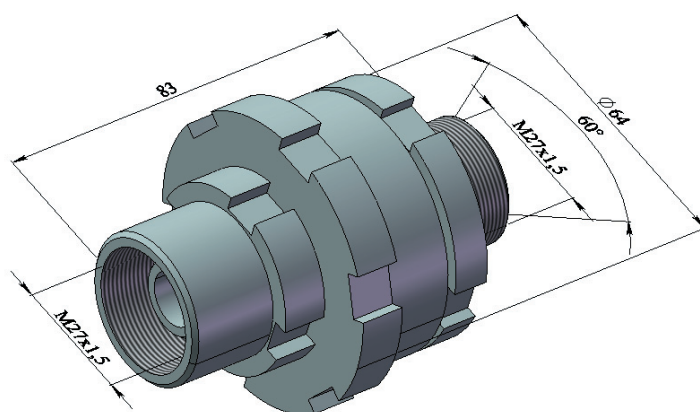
а. Общий вид клапана обратного модуля Ду 12
